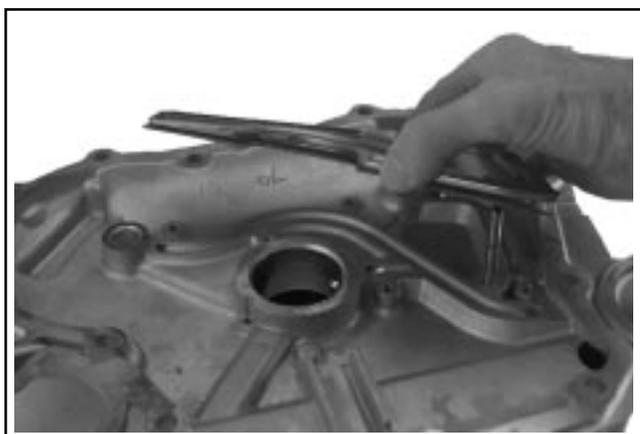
Dépose du couvercle du canal d'huile et du joint.
